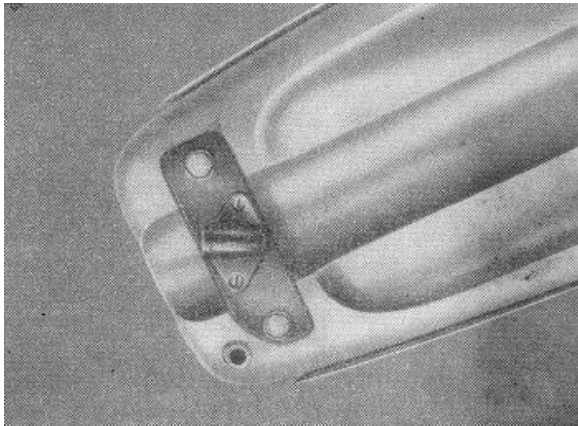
So ist das Halteblech mit Steckerbuchse unter dem Kraftstoffbehälter montiert
